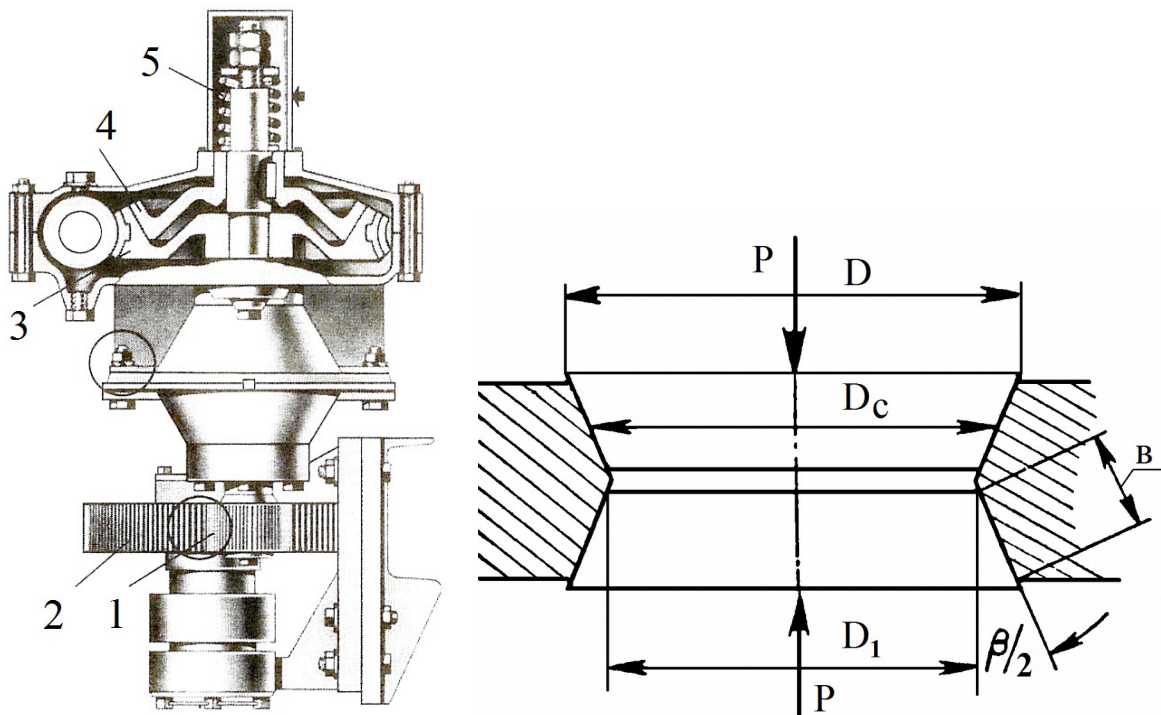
Фрикційна запобіжна муфта редуктора механізму повороту стріли крана:
